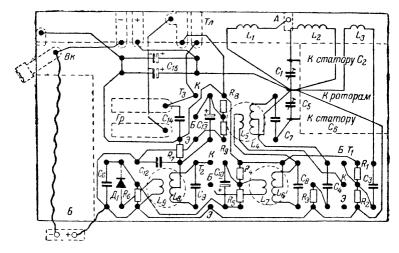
Схема соединений опорных точек деталей на монтажной плате.
